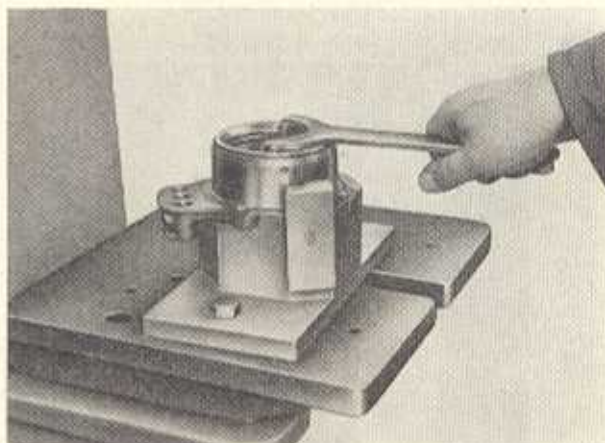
Ringmutter zur Flanscbuchse heraus- bzw. hineindrehen
